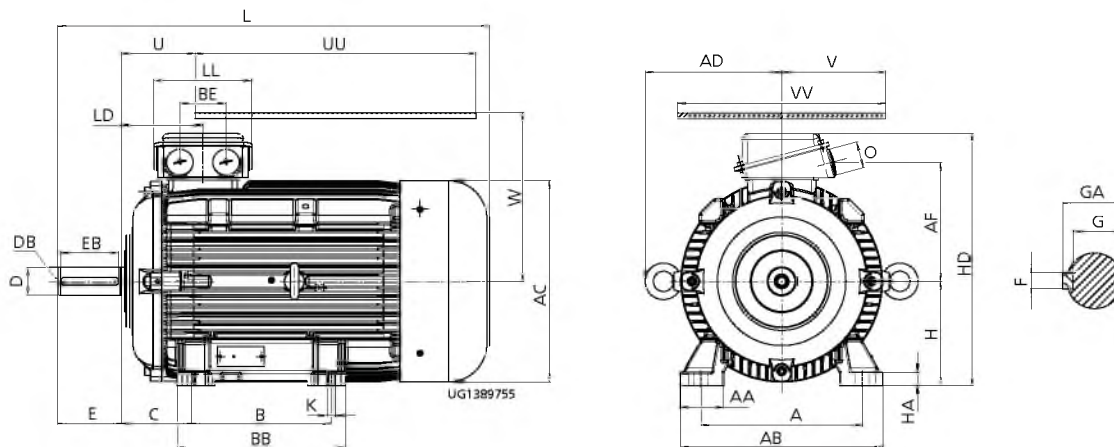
Двигатель с клеммной коробкой со стандартной крышкой подшипников (B3,...)
